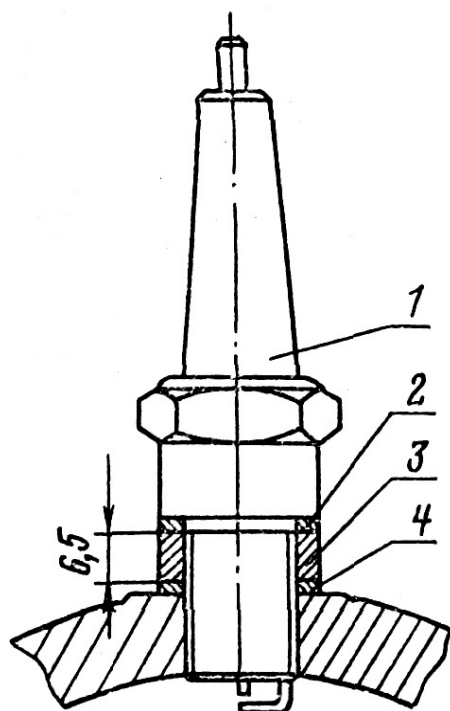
Установка свечи с длиной резьбовой части 19 мм:
